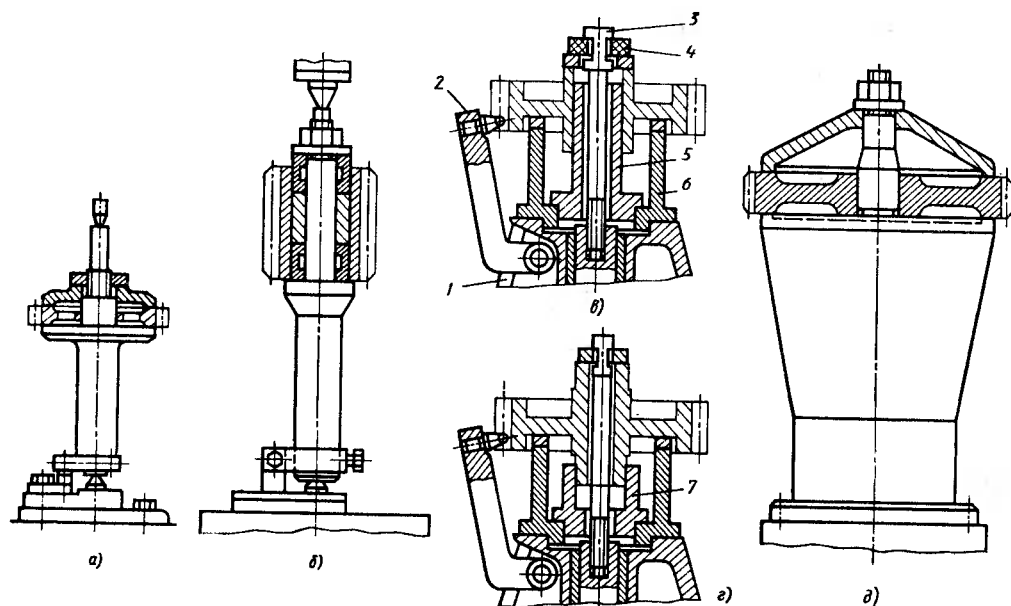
Схемы установки заготовок зубчатых колес на зубошлифовальном станке с вертикальной осью заготовки:
